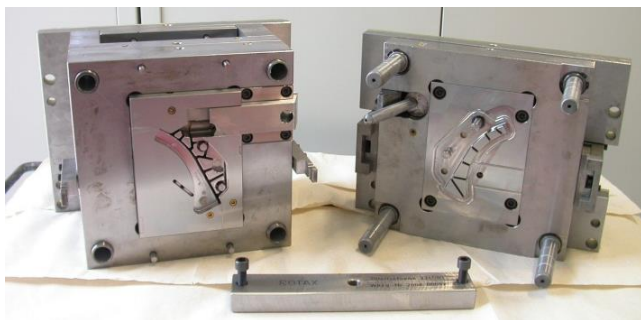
Formhälften eines einfachen Spritzgießwerkzeugs
